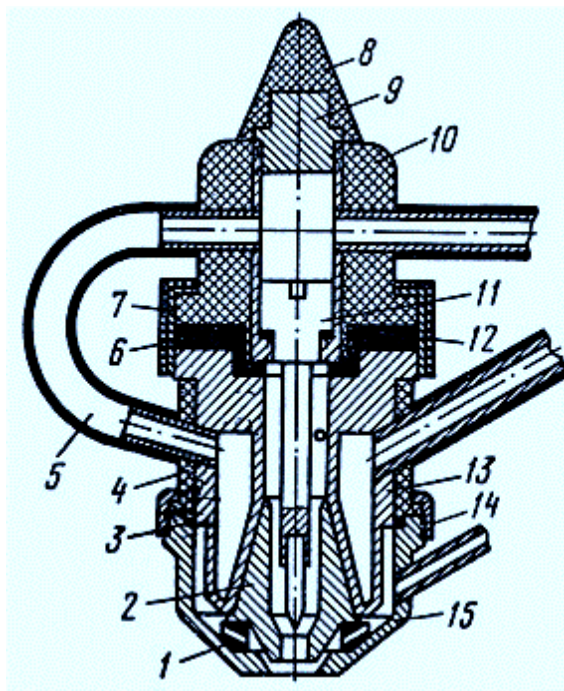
Конструкция горелки для плазменно-дуговой резки:
